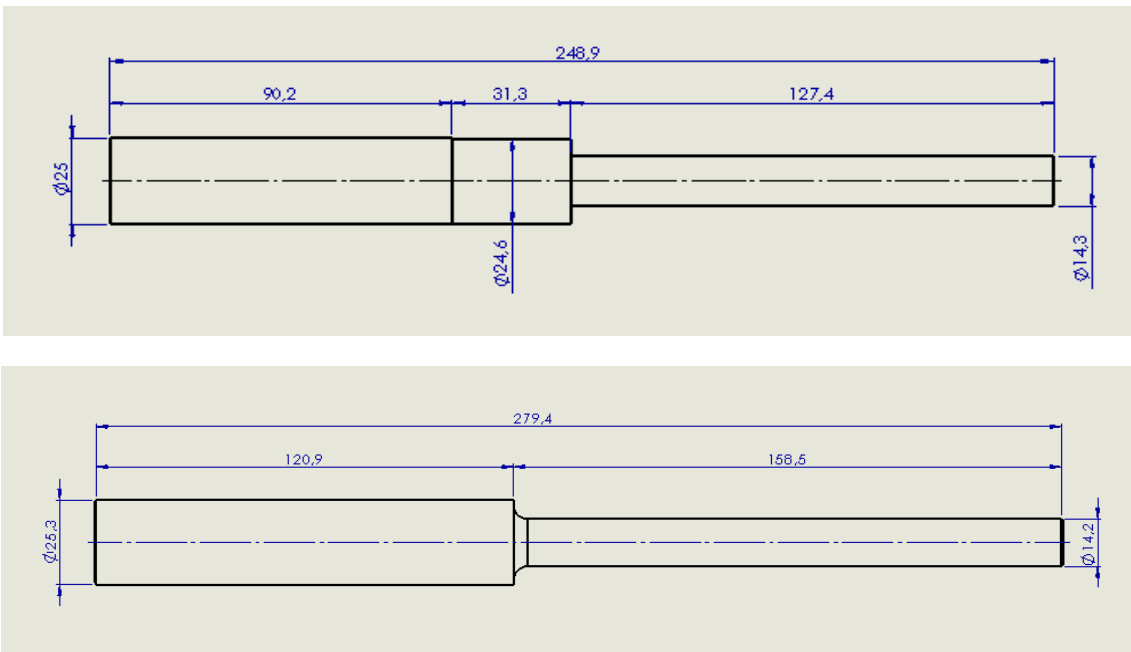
Planos de eje principal. a) Mecanizado en primera configuración, b) mecanizado en segunda configuración.
